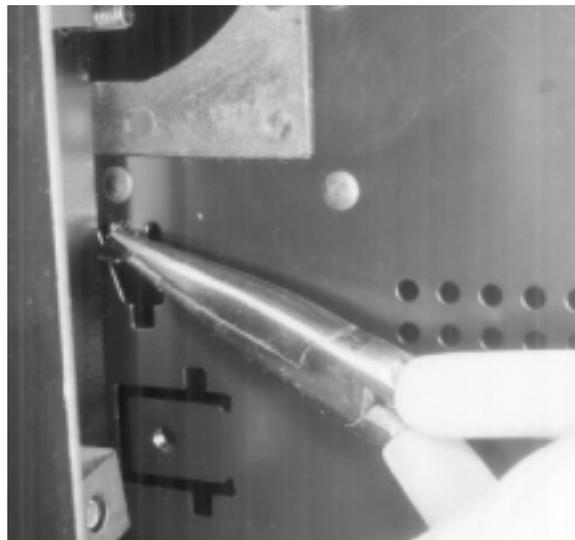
DOBLADO DE ETIQUETAS DE MONTAJE
